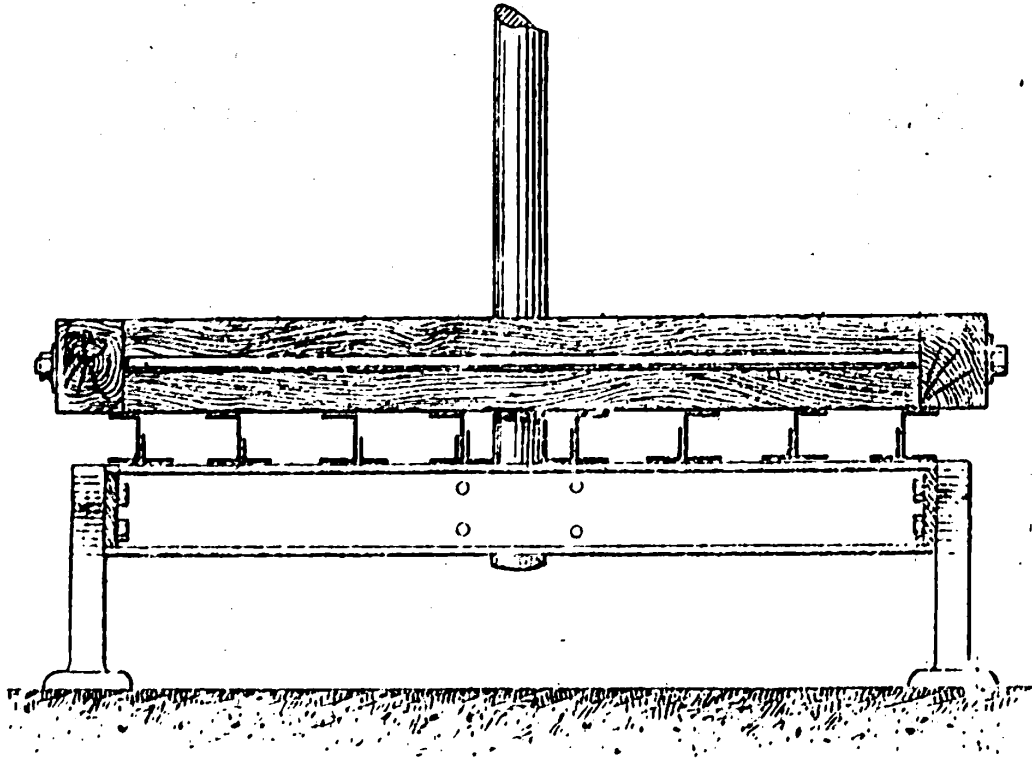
PRESSEIRS SUR PIED. Maie en chêne à serrge, couvercle en bois sous marc, charpente et estaudet entièrement en fer, vis de 3<sup>m</sup>00, appareil de serrage renforcé du type Mabilie ou Marmonier, au choix du client.
